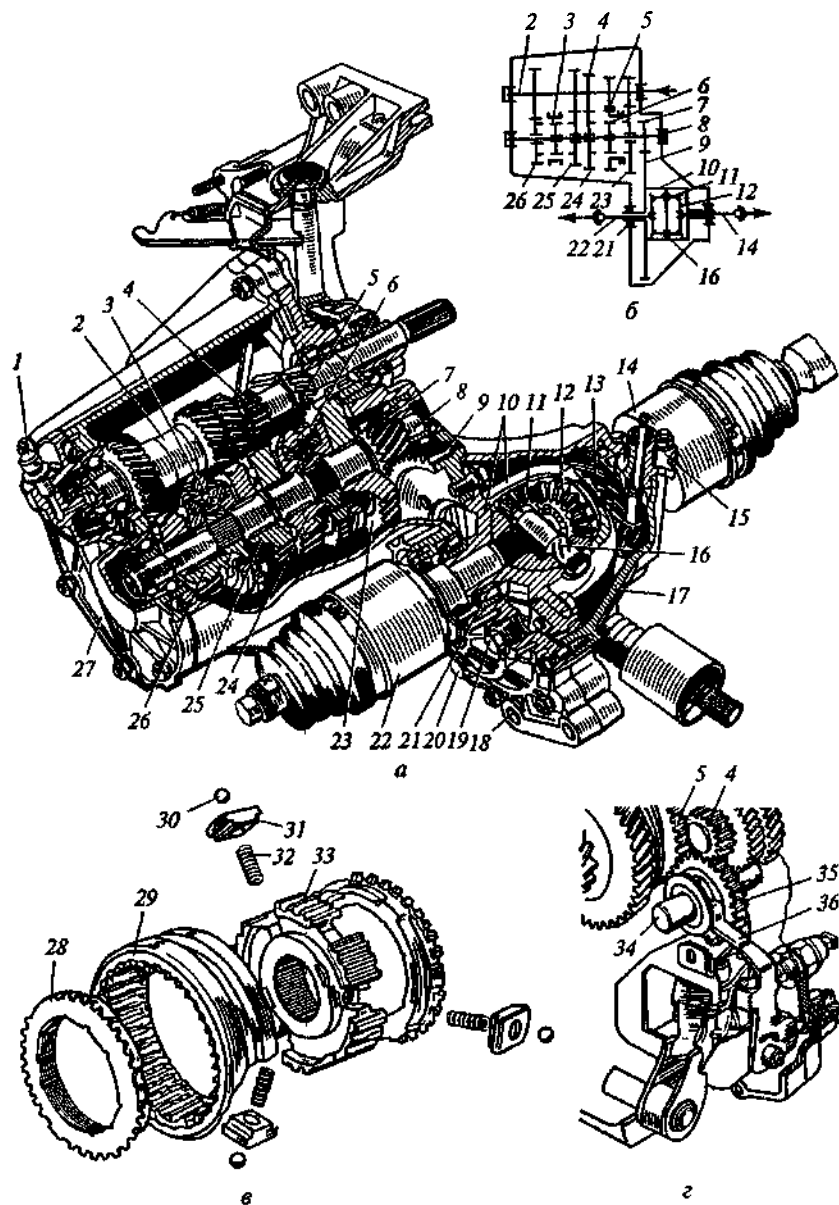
Коробка передач переднеприводного легкового автомобиля ВАЗ: а — общий вид; б — схема; в — детали синхронизатора; г — механизм включения заднего хода; 1 — сапун; 2 — первичный вал; 3 и 6 — синхронизаторы; 4, 7, 9, 12, 13, 23... 26 и 35 — шестерни; 5 — зубчатый венец; 8 — вторичный вал; 10 — корпус; 11 — сателлит; 14 и 22 — шарниры; 75 — привод спидометра; 16 и 34 — оси; 17 и 18 — картеры; 19 и 20 — пробки; 21 — подшипник; 27 — крышка; 28 — кольцо; 29 — муфта; 30 — фиксатор; 31 — сухарь; 32 — пружина; 33 — ступица; 36 — вилка
